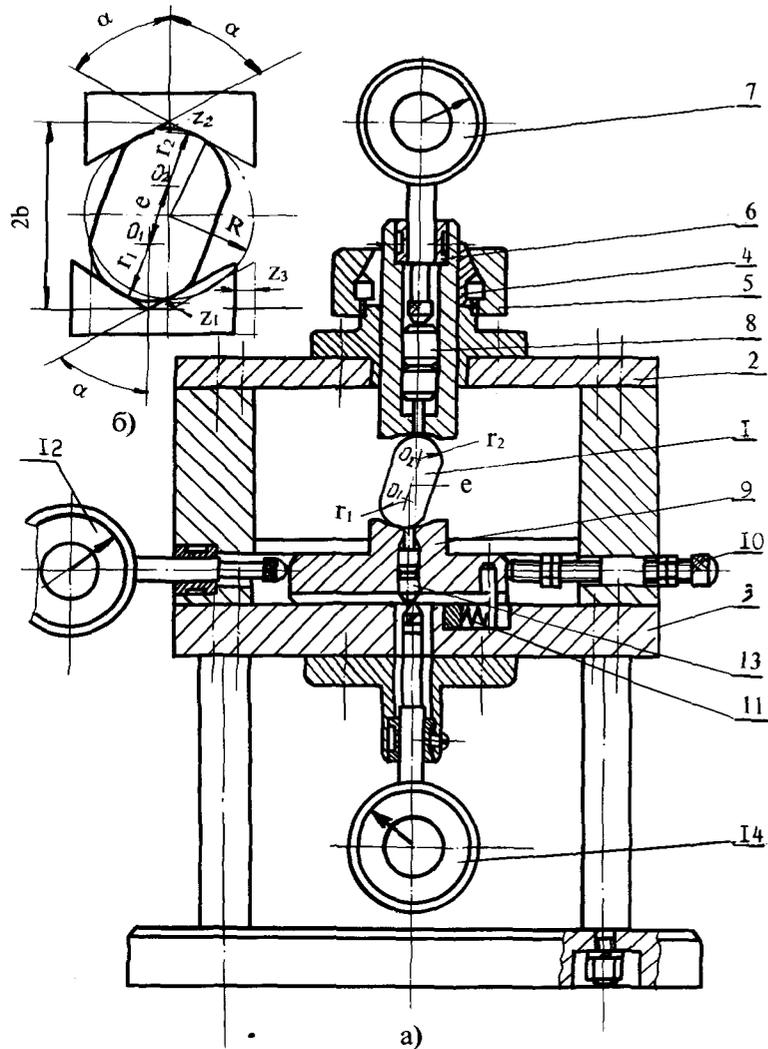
Приспособление для контроля размеров эксцентриковых роликов:
